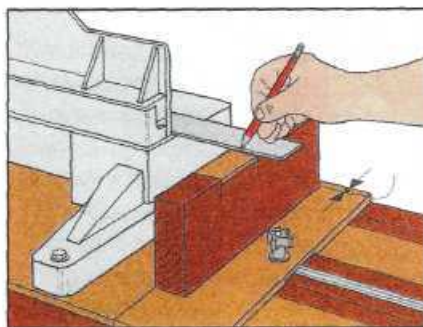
Разметка выборки в суппорте под направляющую линейку.
